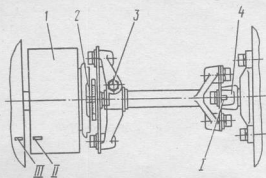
Установка начала впрыска топлива в первом цилиндре двигателя по меткам:
